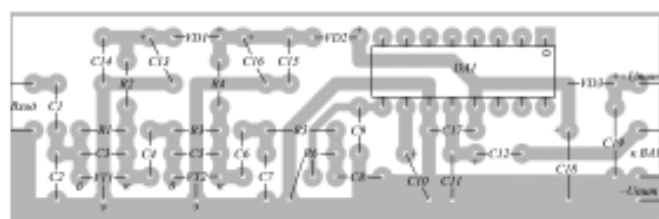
Ультразвуковой приёмник. Эскиз монтажной платы блока усилителя ЗЧ. Вид со стороны установки деталей
